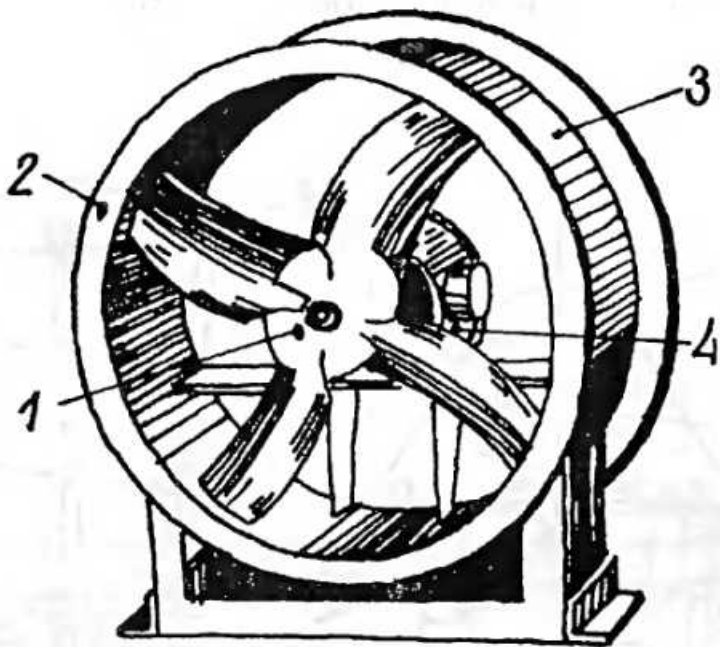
Осьовий вентилятор:1 - робоче колесо; 2 - фланець; 3 - циліндричний корпус; 4- електродвигун
